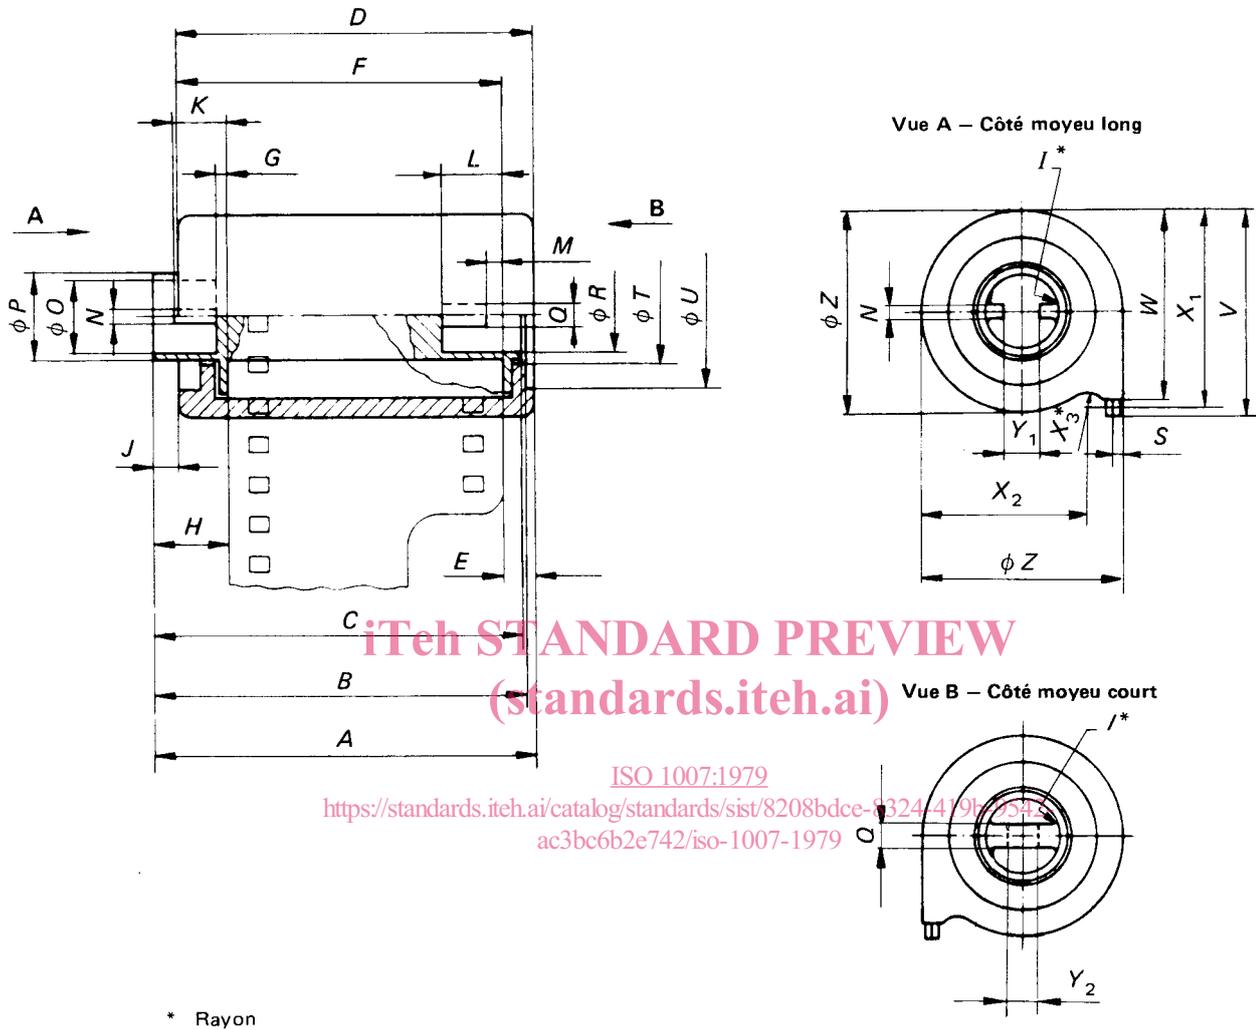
Dimensions de la cartouche pour film de format 135
